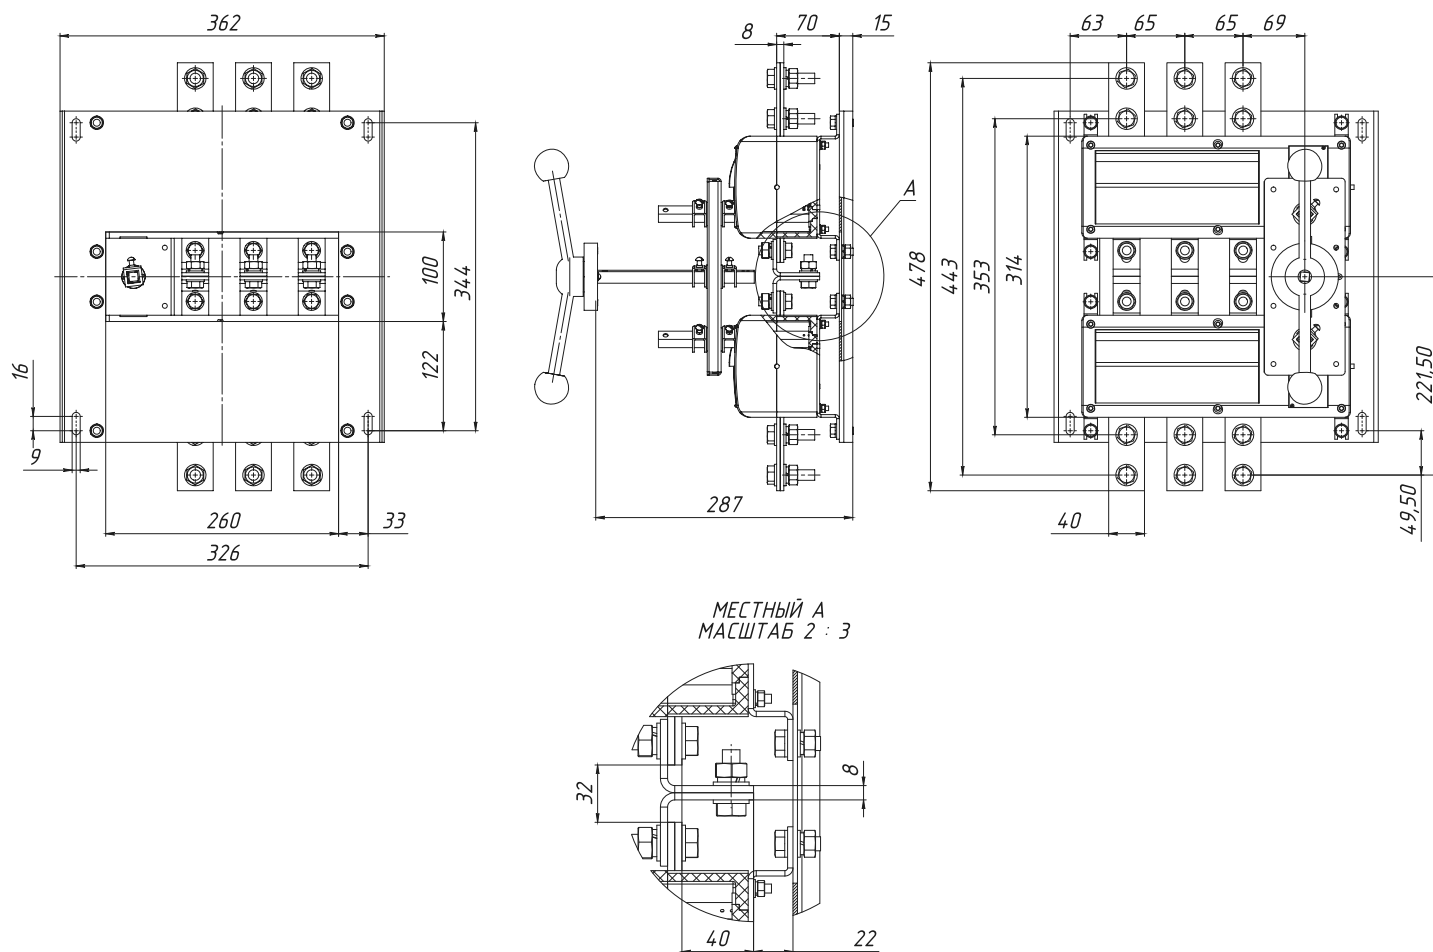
Выключатель-разъединитель ВНК-39-71130-32 УХЛ3 на два направления, масса не более – 14,5 кг
